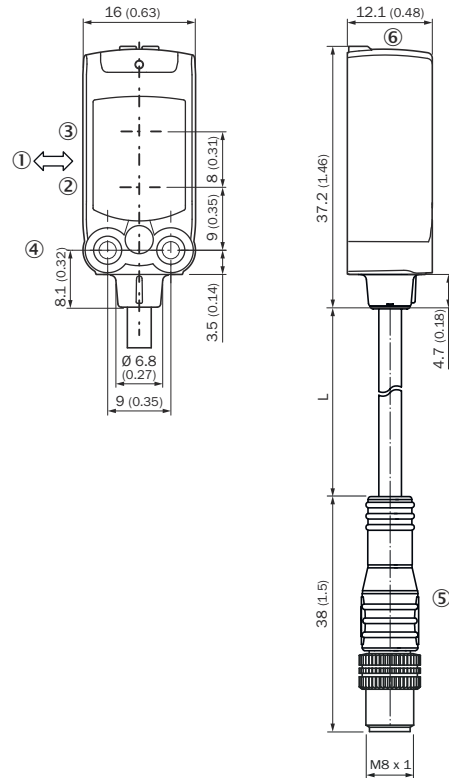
Desenho dimensional, cabo com conector macho M8, união roscada recartilhada
